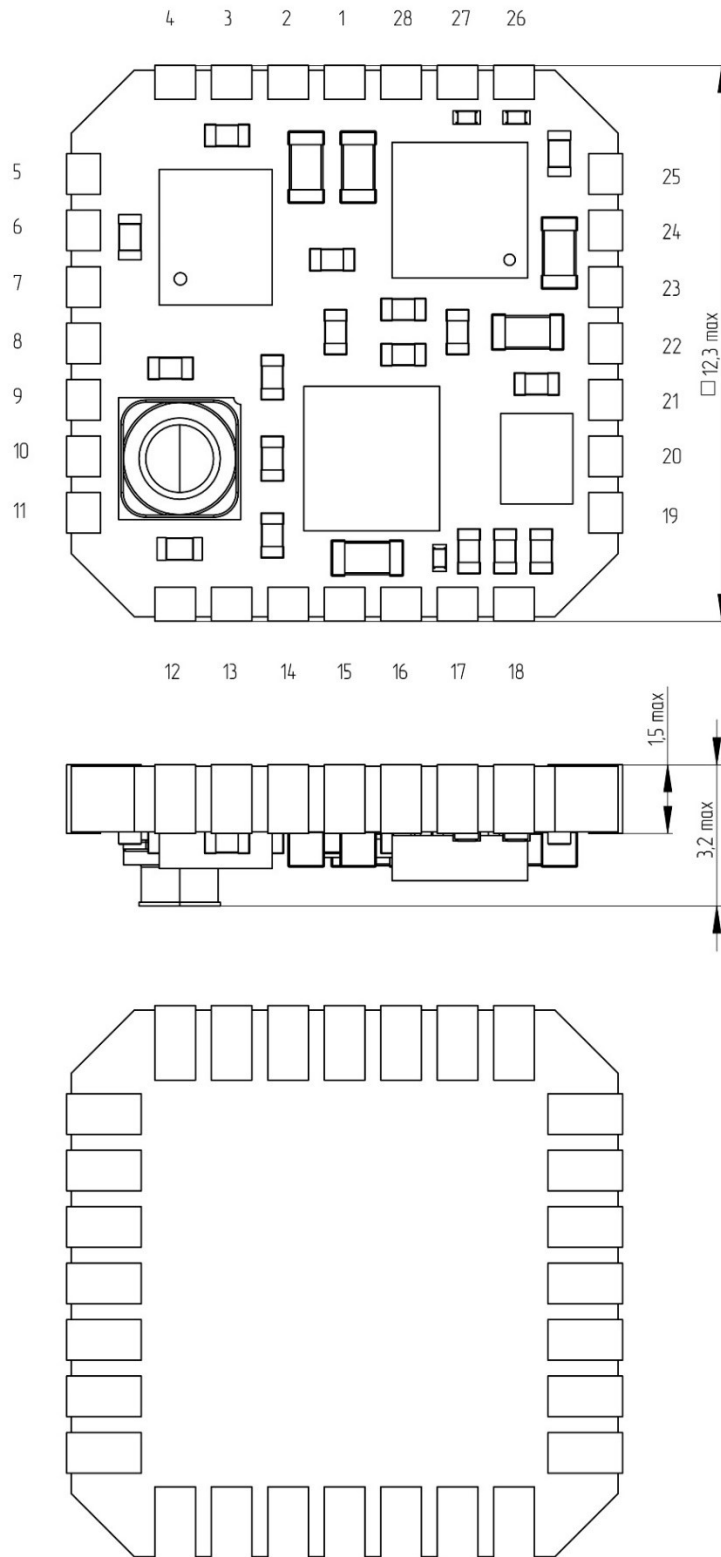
Габаритный чертёж ГКВ-0
